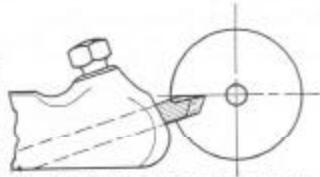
Posição do ferro de corte para facear o extremo dum veio
